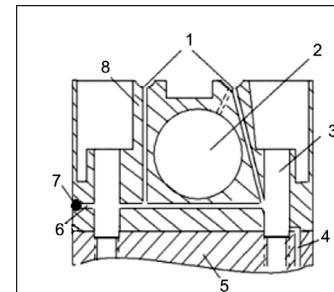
Схема смазки головки блока цилиндров:
